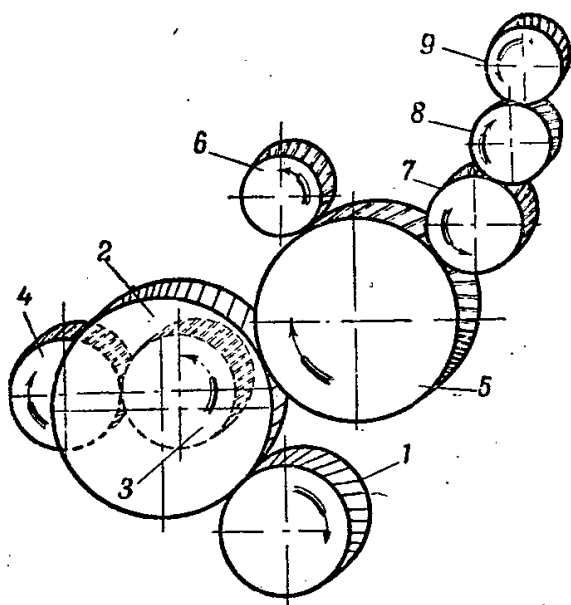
Схема расположения шестерён в кожухе распределительных шестерён:
